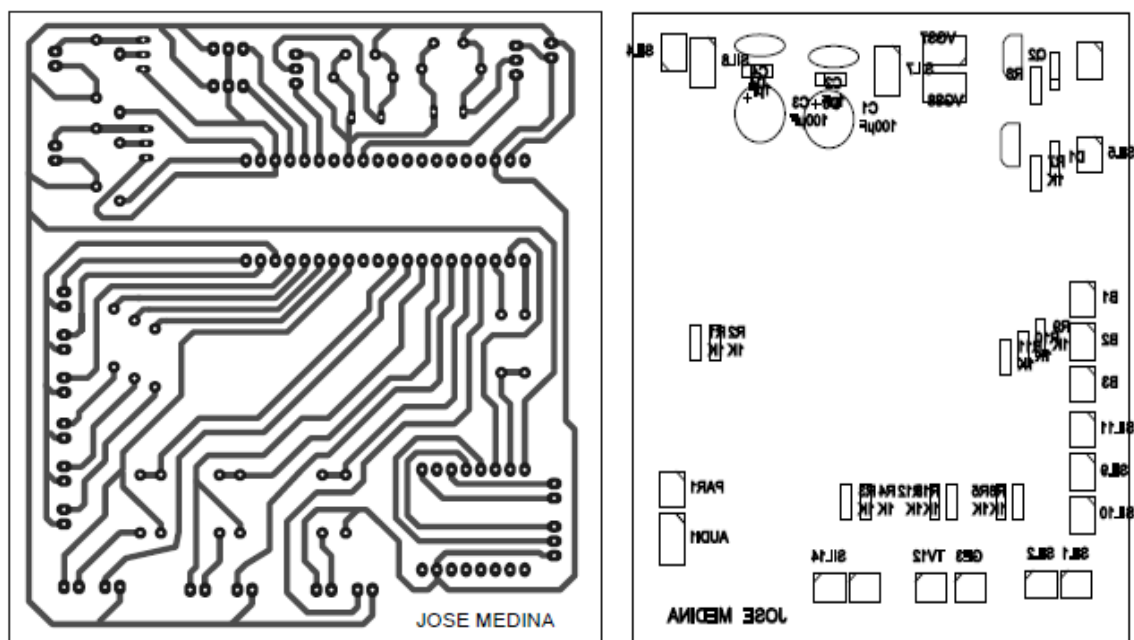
Diseño de la placa (PCB) en PCBWizard.
